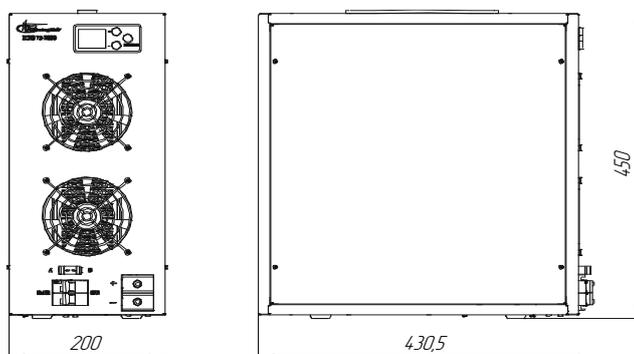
Габаритный чертеж НЭВ 75-2000
